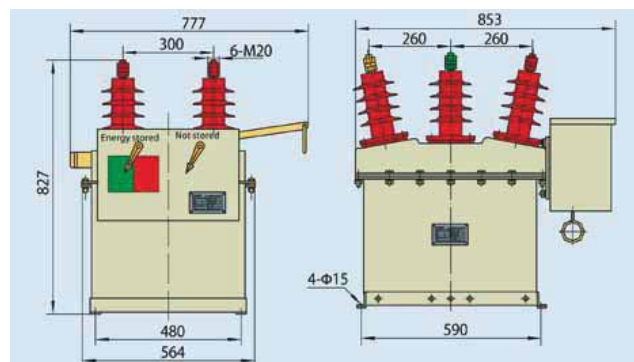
Внешний вид и размеры выключателя ZW8-12
